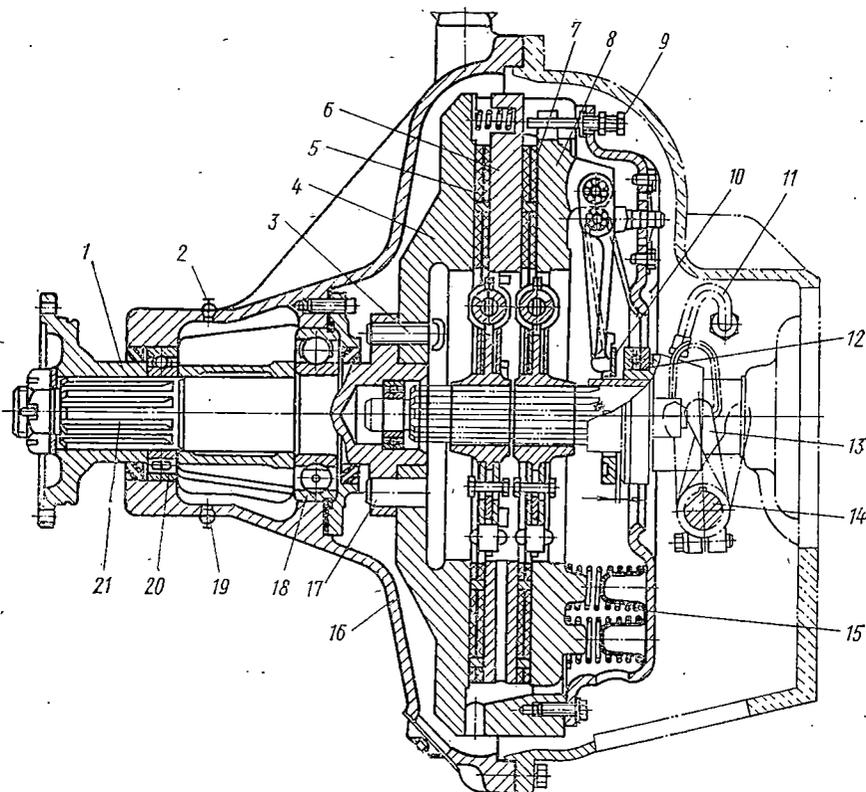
Муфта сцепления самоходного скрепера ДЗ-11М:
